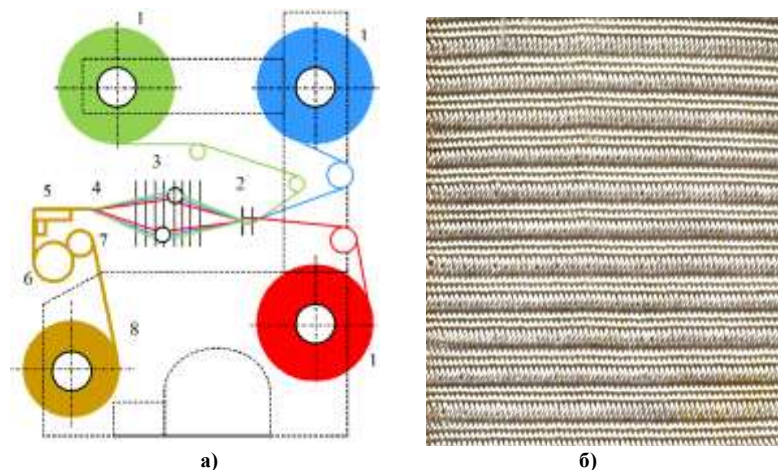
Загальний вигляд: а) схема заправки ткацького верстата: 1 – ткацький навій; 2 – пристрій контролю обриву основної нитки; 3 – ремізні рамки механізму утворення зіву; 4 – зона формування багатошарової технічної тканини; 5 – напрямна; 6 – вал'ян; 7 – вал для стиснення тканини; 8 – вал для намотування тканини; ■ – в'язуча основа; ■ – наповнювальна основа; ■ – корінна основа; ■ – багатошарова технічна тканина; б) зовнішній вигляд п'ятишарової тканини
